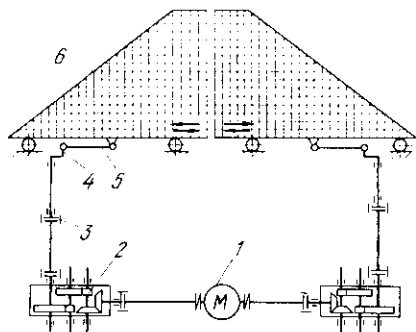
Кинематическая схема привода раздельного рыхлителя: 1 — двигатель; 2 — редуктор; 3 — муфта; 4 — кривошип; 5 — шатун; 6 — рыхлитель
